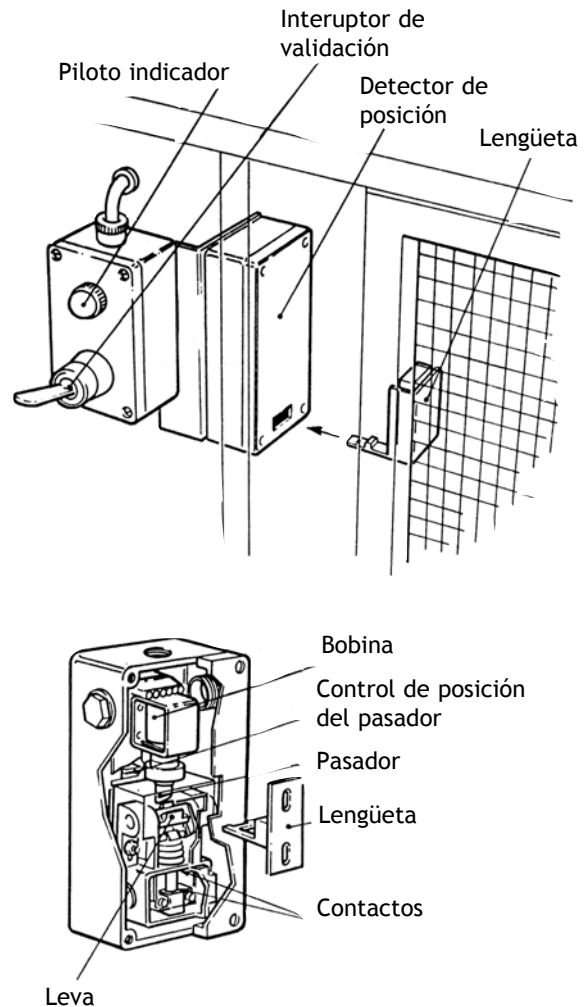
Resguardo móvil con dispositivo de enclavamiento.
